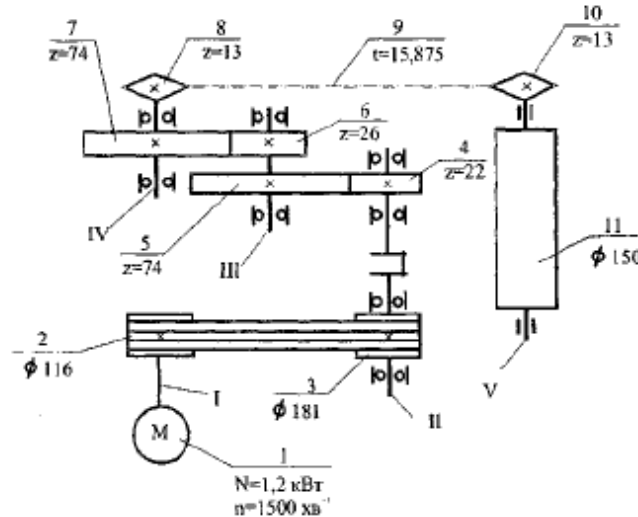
Кінематична схема механізму подачі деревообробного верстата
